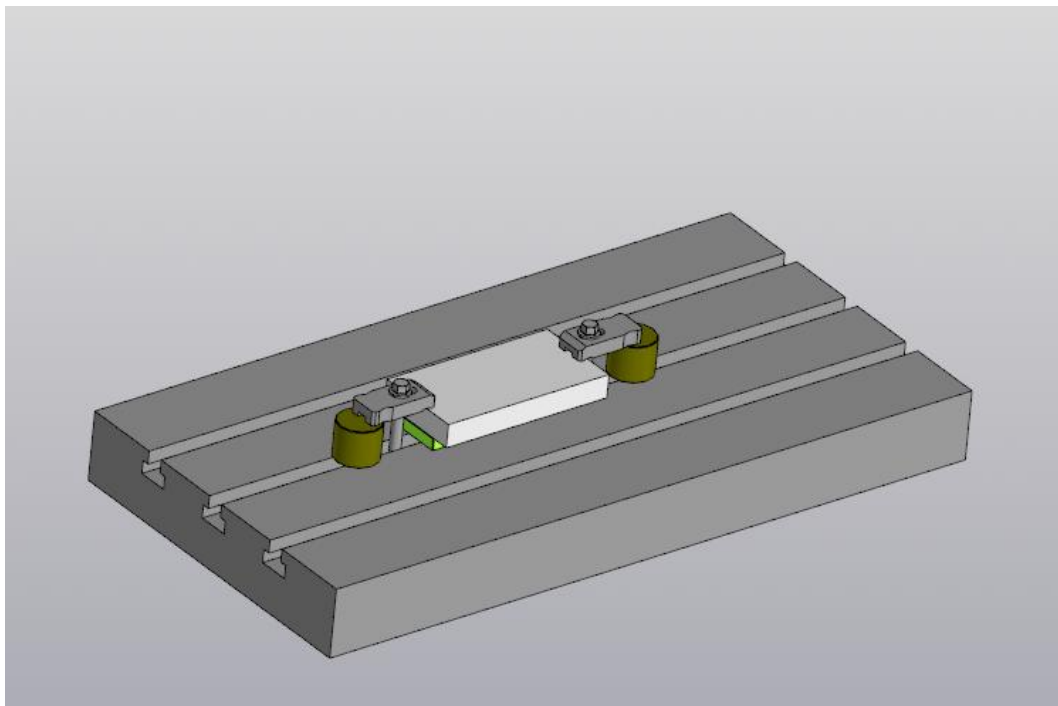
Закріплення заготовки на столі верстата Chiron Mill800
